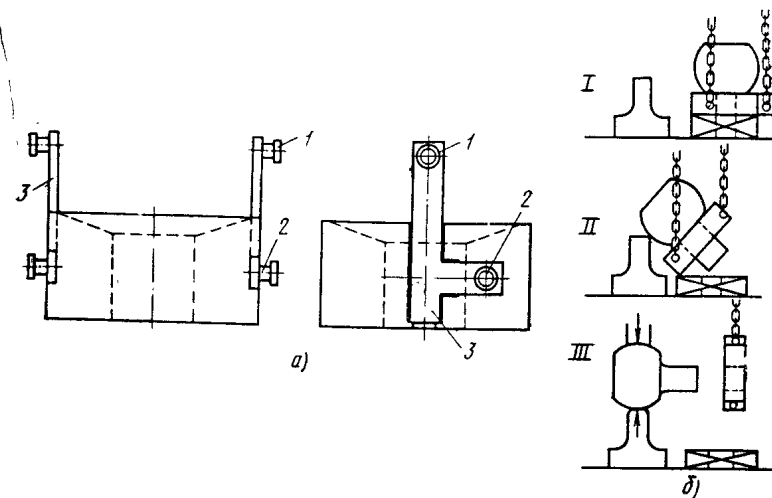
Осадочно-кантовочная плита конструкции Левандовского и Ткаченко:
